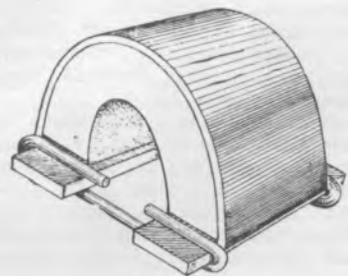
Заготовка, заклепанная скобками и загнутая вместе с шинкой.
